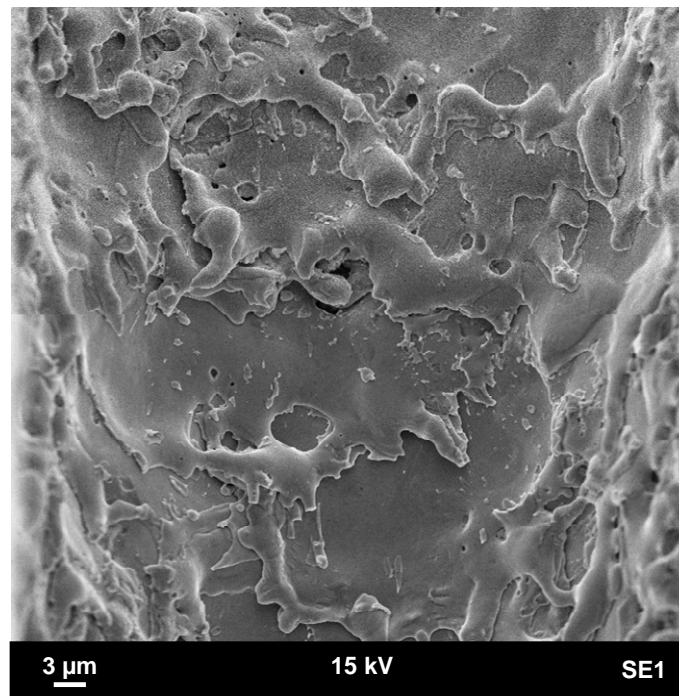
Fond d'entaille en U brut d'usinage par électro-érosion
